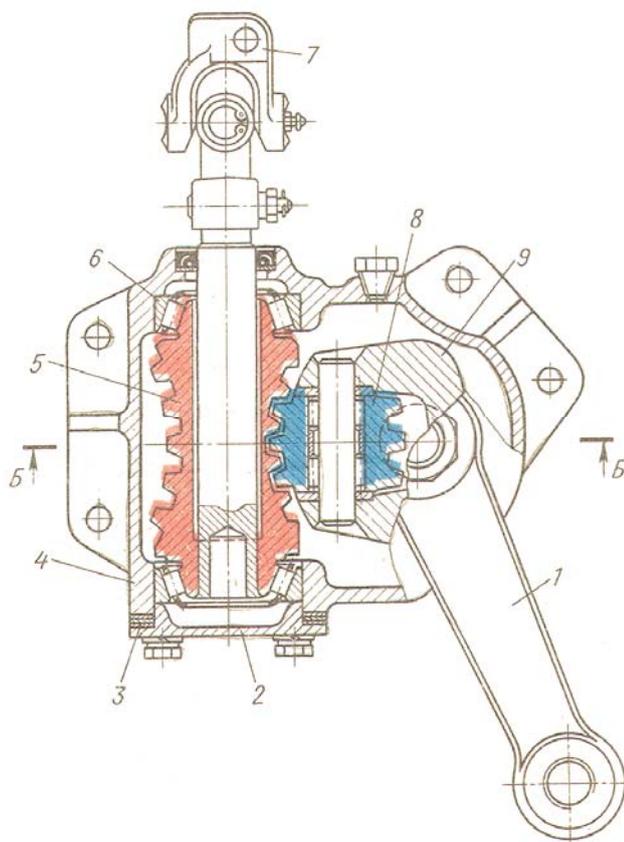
Рулевой механизм автомобиля КАЗ-6086: 1 – рулевая сошка; 2 – крышка; 3 – прокладки; 4 – чугунный картер; 5 – червяк; 6 – подшипники; 7 – карданный шарнир; 8 – трёхрёберный ролик; 9 – вал
